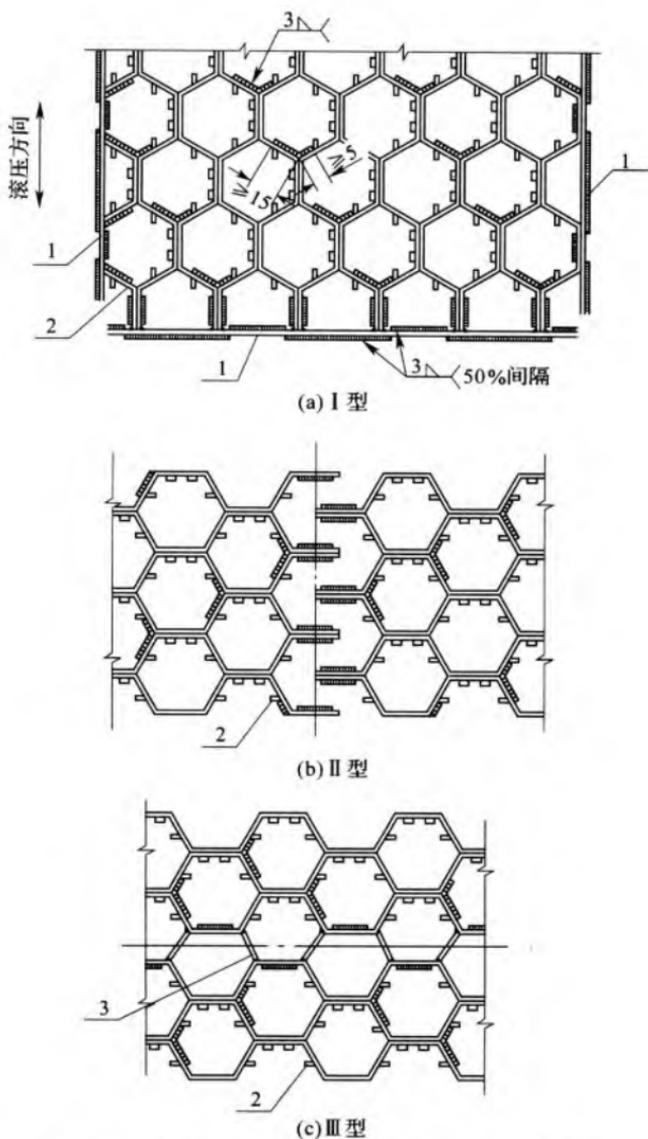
与器壁焊接的龟甲网拼接及焊缝布置示意
